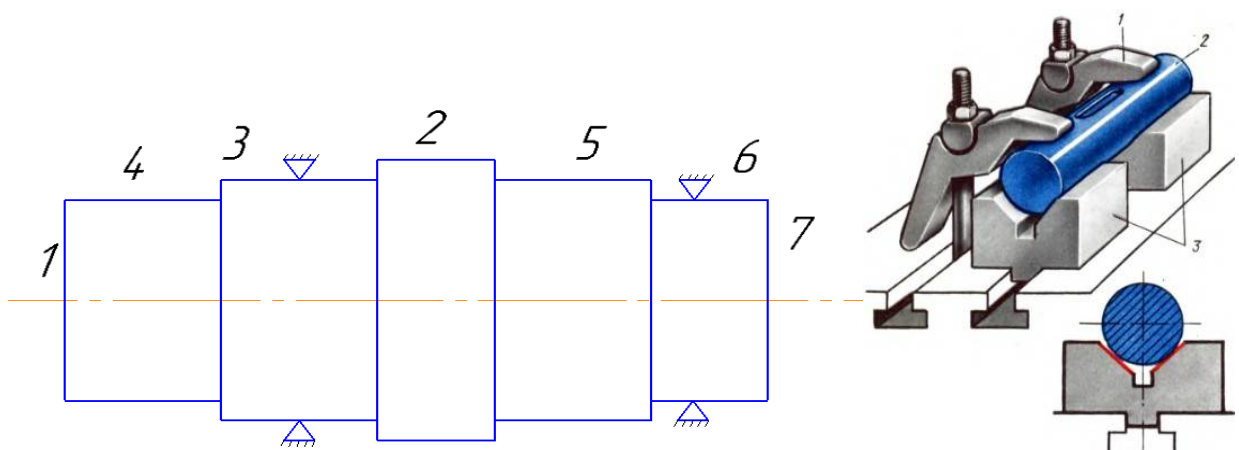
Позиція 11: 1 – затискачі; 2 – деталь; 3 – призми
